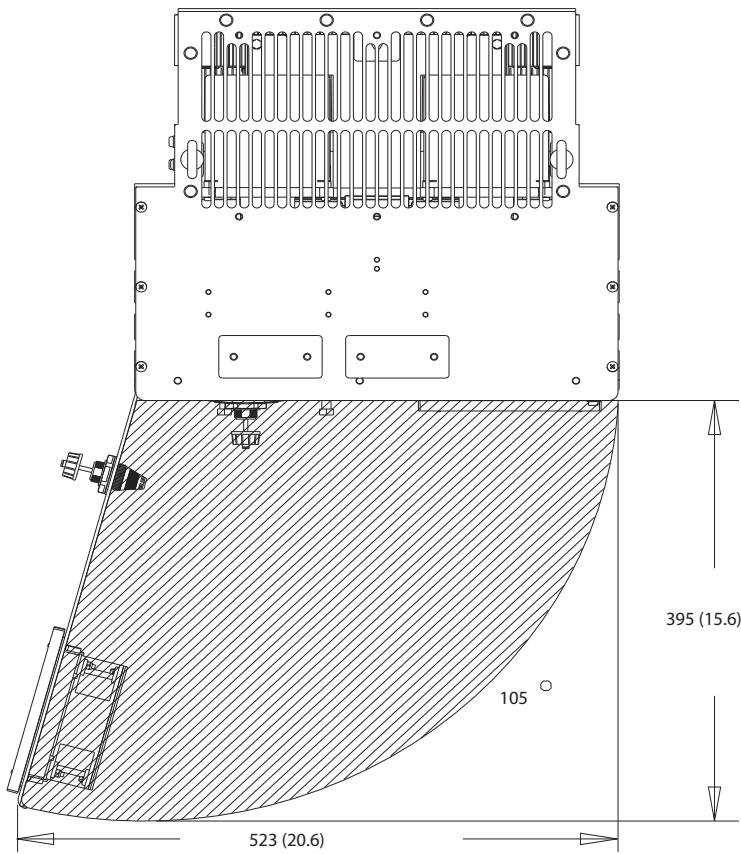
Dimensi Akses Heat Sink untuk D7h
